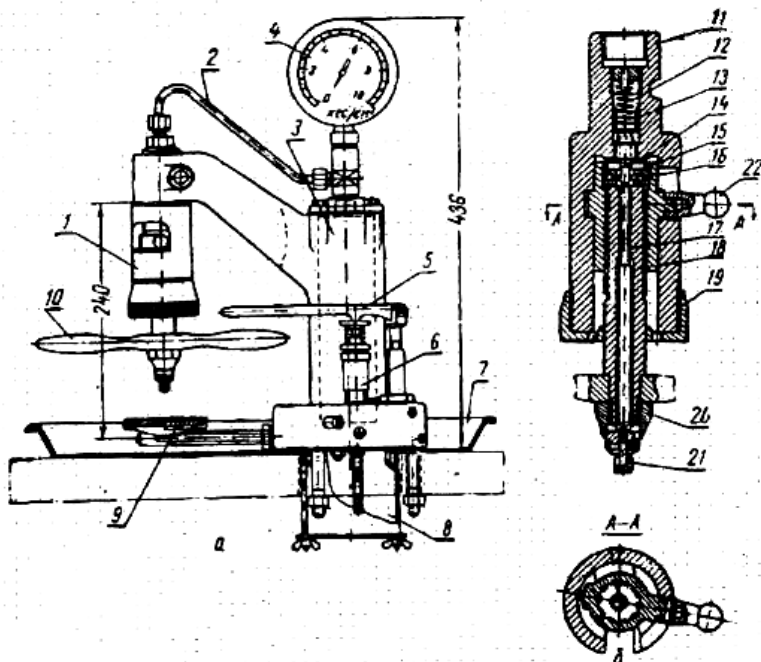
Прибор КИ-1086 (ПНК) Для испытаний нагнетательных клапанов топливных насосов: а – общий вид прибора; б – разрез устройства для крепления нагнетательного клапана; 1 – устройство для крепления нагнетательного клапана; 2 – трубка; 3 – гидравлический аккумулятор; 4 – манометр; 5 – рукоятка; 6 – подкачивающий насос; 7 – противень; 8 – банка; 9 – воронка; 10 – рукоятка; 11 – корпус; 12 – пружина; 13 – поршень; 14 – испытуемый клапан с прокладкой; 15 – втулки; 16 – упорный шарикоподшипник; 17 и 18 – винты; 19 и 10 – гайки; 21 – микрометрический винт; 22 – рукоятка
